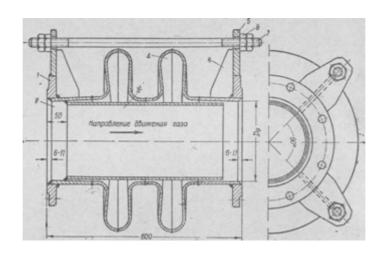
Линзовый компенсатор. 1 - фланец; 2 - патрубок; 3 - рубашка; 4 - полулинза; 5 - лапа; 6 - ребро; 7 - тяга; 8 – гайка
